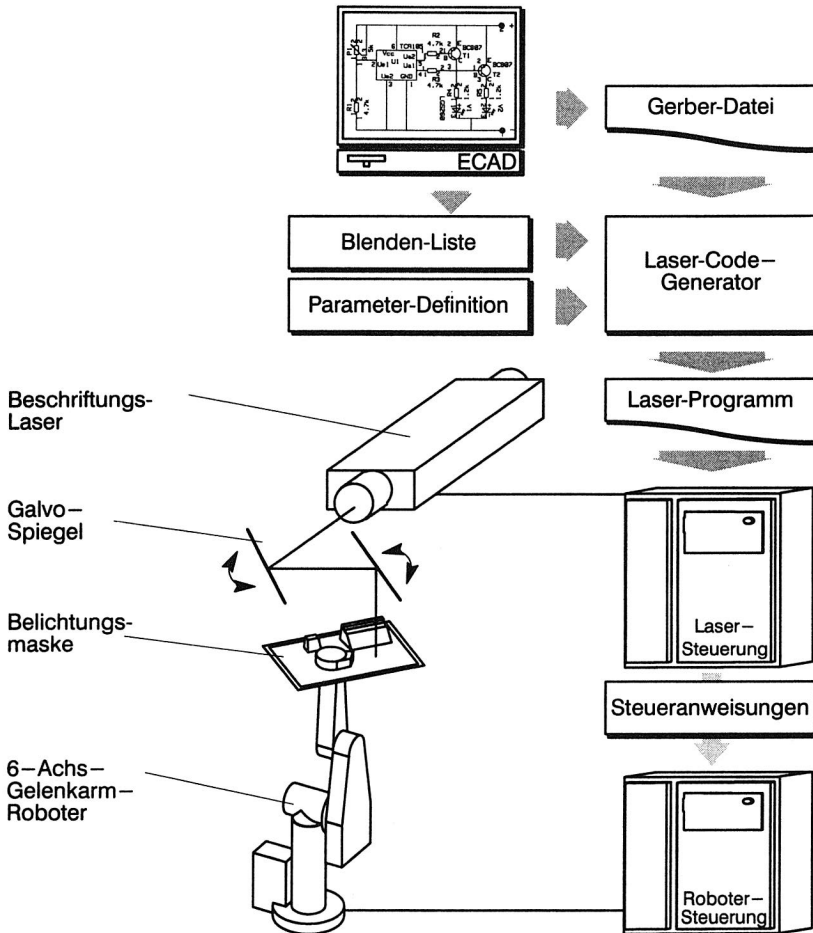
CAD/CAM-Verfahrenskette für die 3D-Laser-Beschriftung
